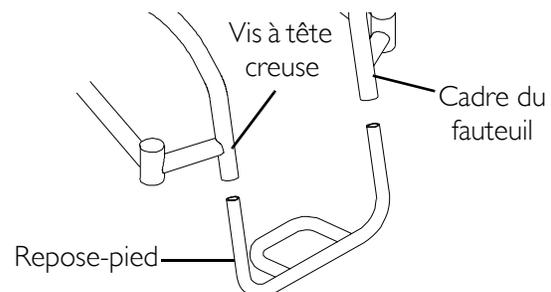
Réglage / Remplacement du repose-pied standard
